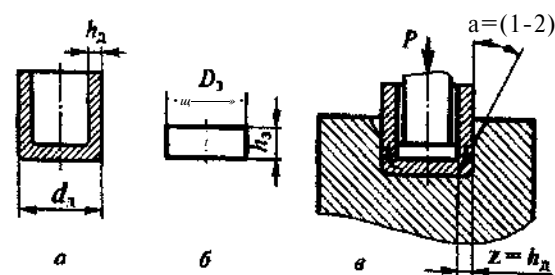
Обратное холодное выдавливание: а - деталь; б - заготовка; в - схема процесса
